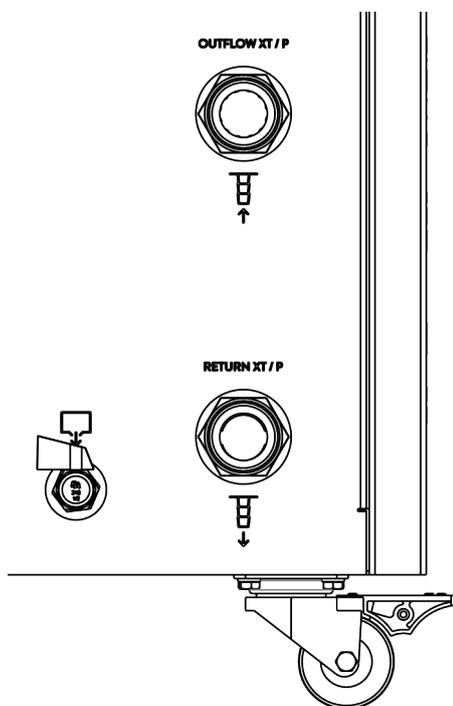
Lato collegamento all'apparecchio di termostatazione
